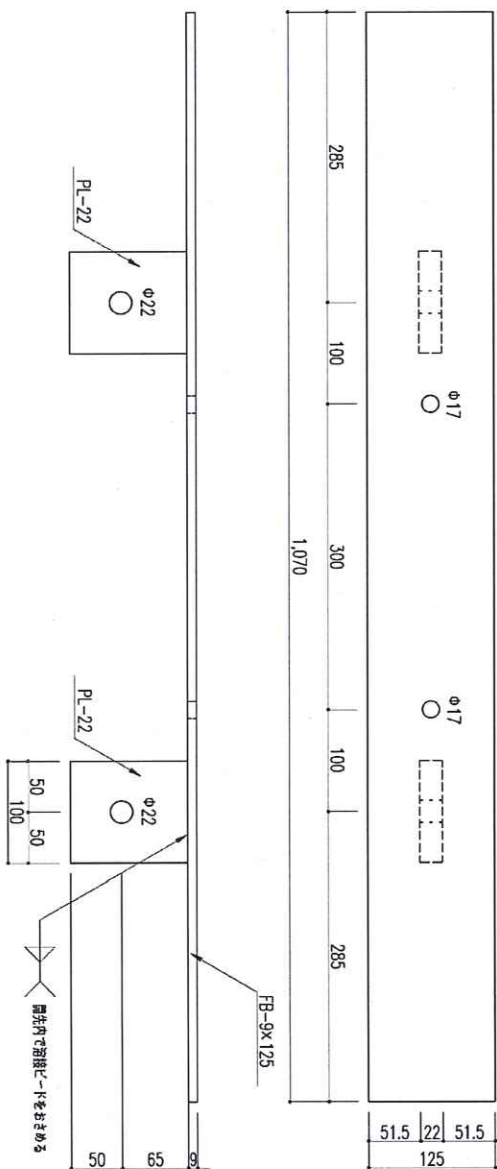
試験法 B 治具部品図 (1) (単位 : mm)
